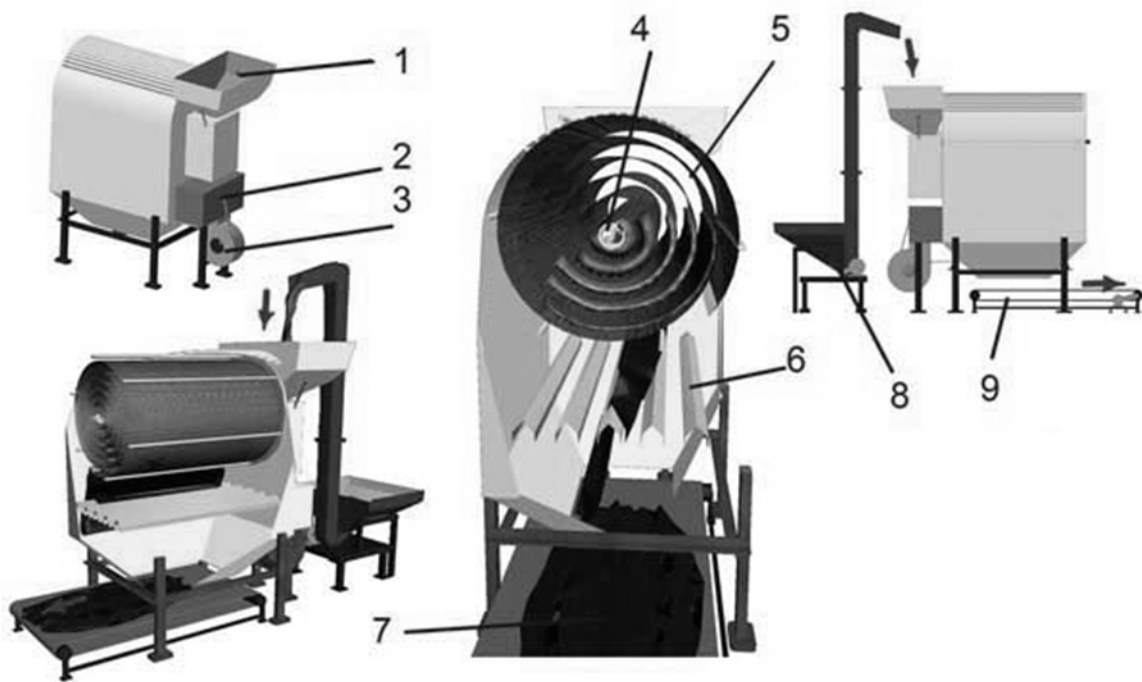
Схема сушарки з спіралеподібною поверхнею:
